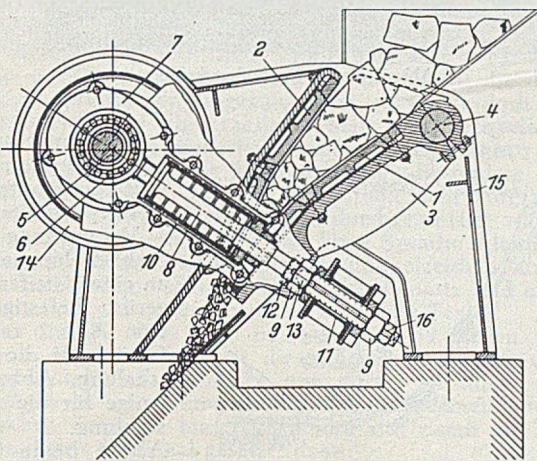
Aufbau des Stahlplatten-Schlagbrechers. Bauart Stahlbau-Rheinhausen.
